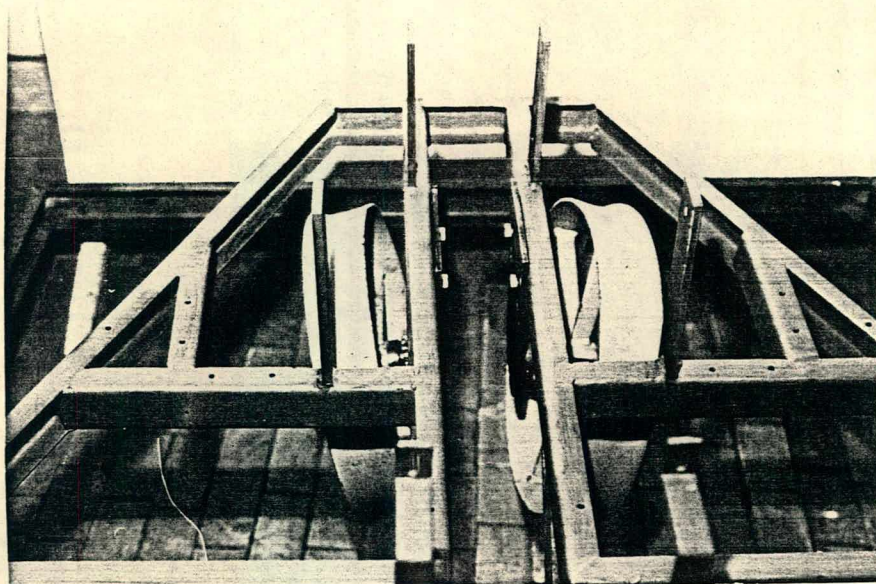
Vista após a montagem das rodas compactadoras.
